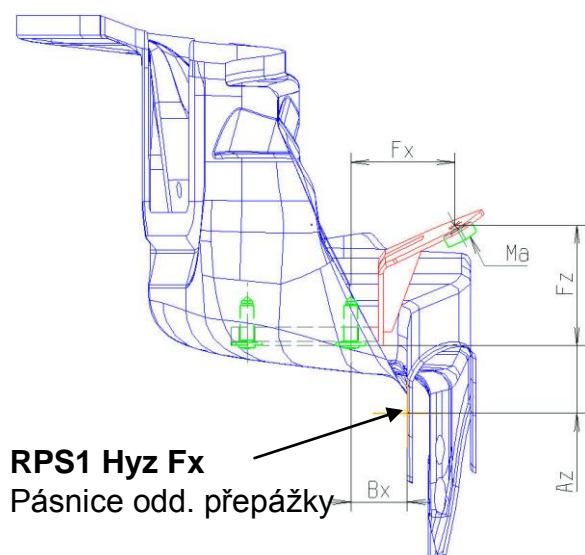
Toleranční řetězec pro bod a, rovina YZ
